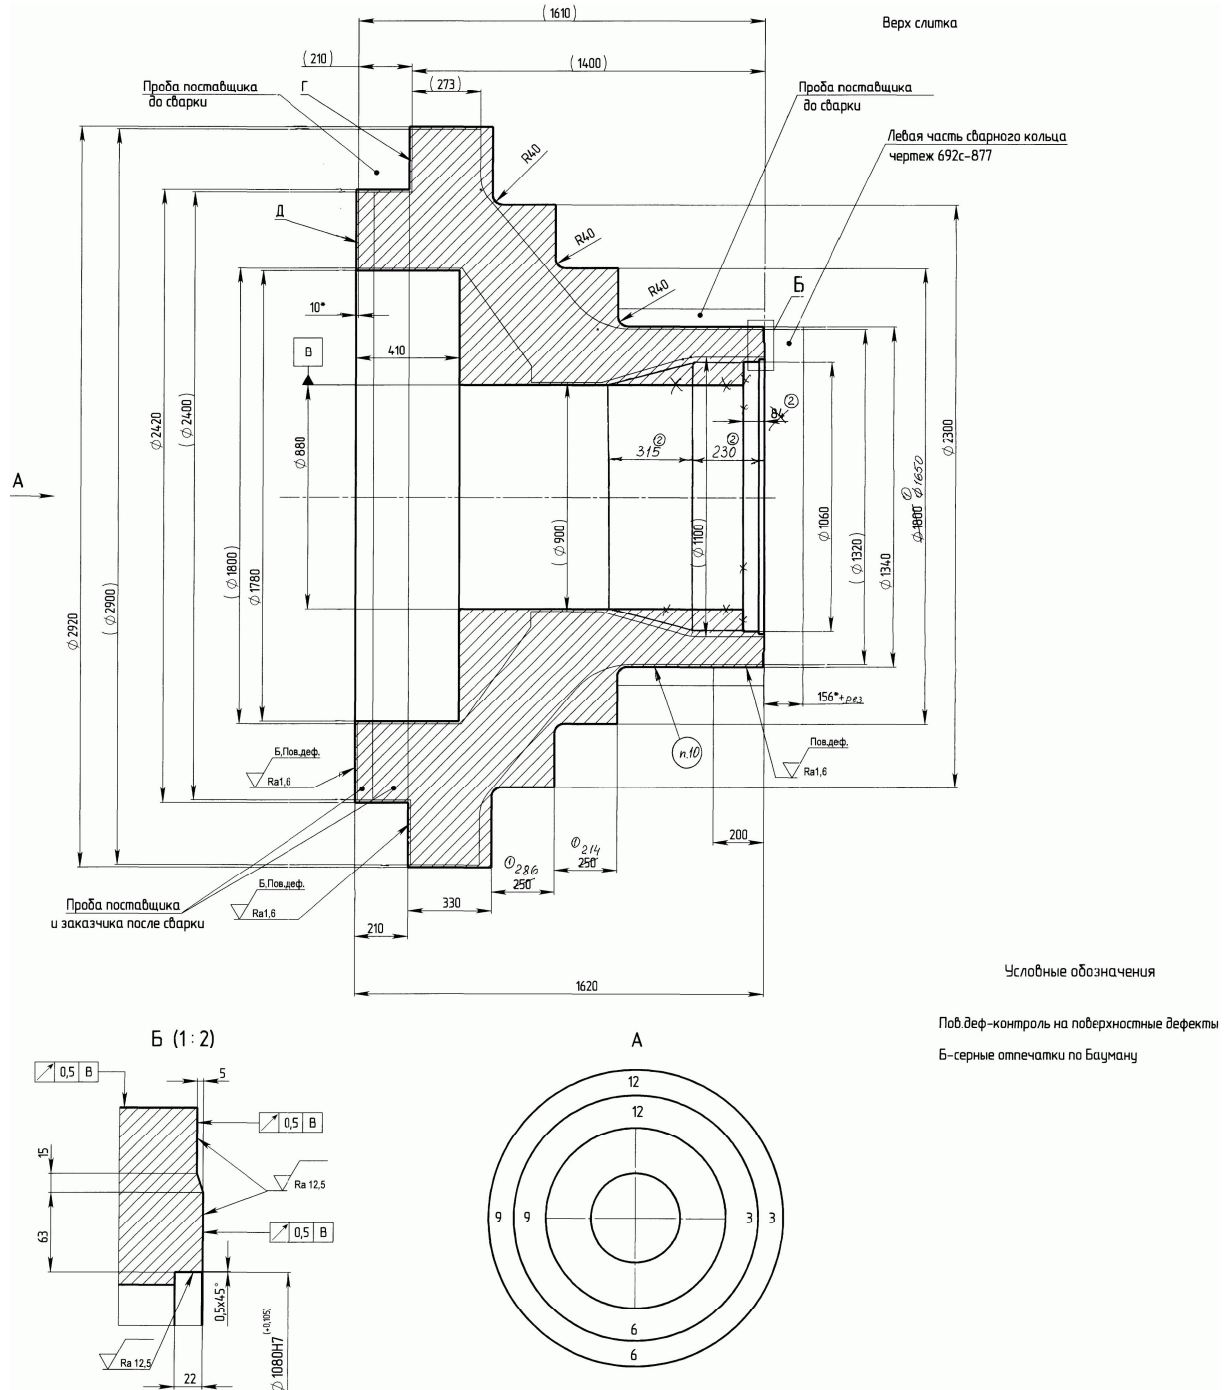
Эскиз расчетной заготовки «Левая часть вала», номер чертежа детали 692с – 874
